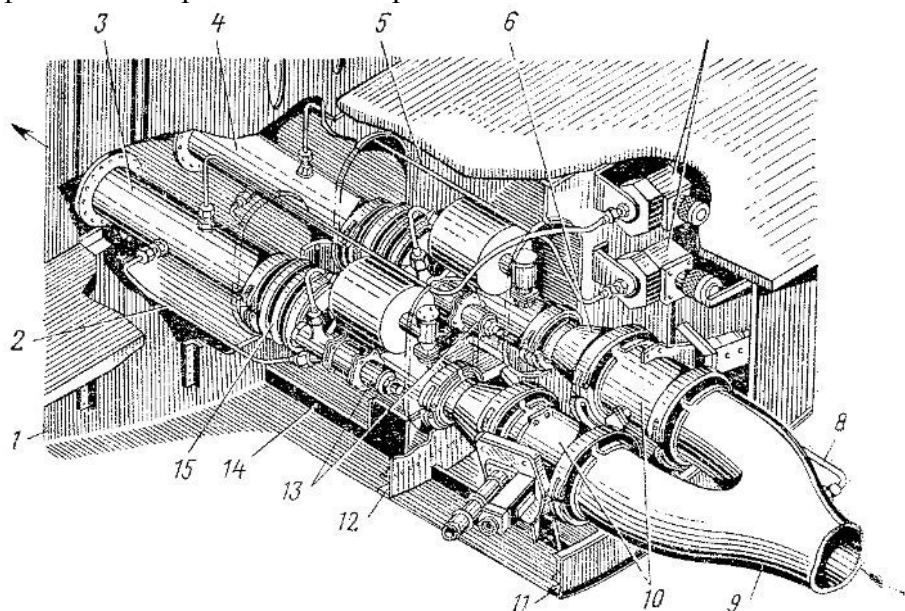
Расположение агрегатов между шп. № 68 и 70:
